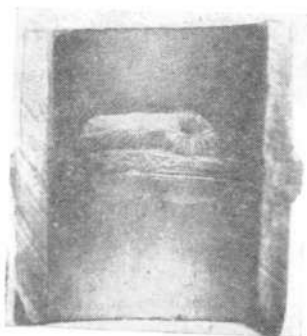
Свищ, образовавшийся в результате резкого обрыва сварочной дуги при сварке вольфрамовым электродом.
